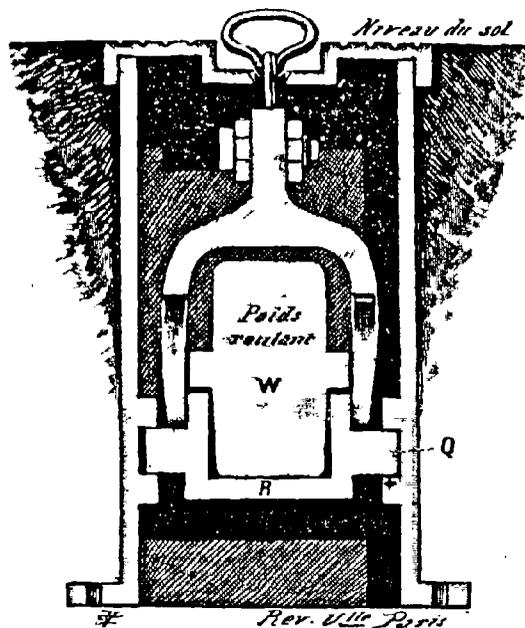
Coupe par la boîte du levier de verrouillage.
